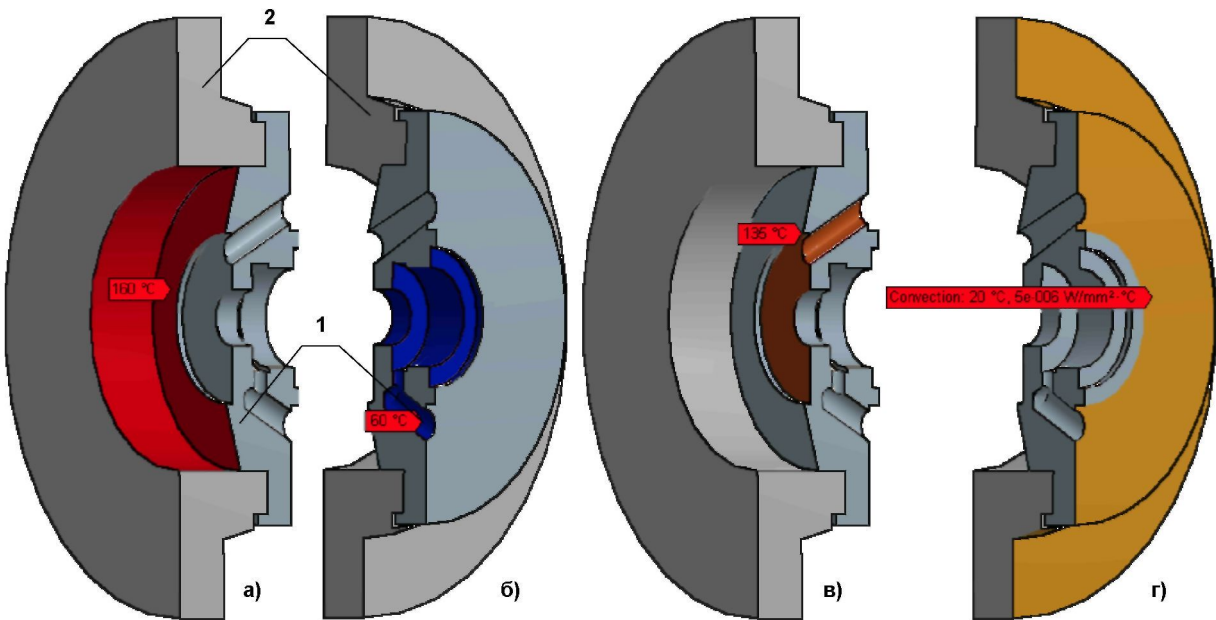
Корпус пускового устройства (1) и часть крышки насоса (2)
